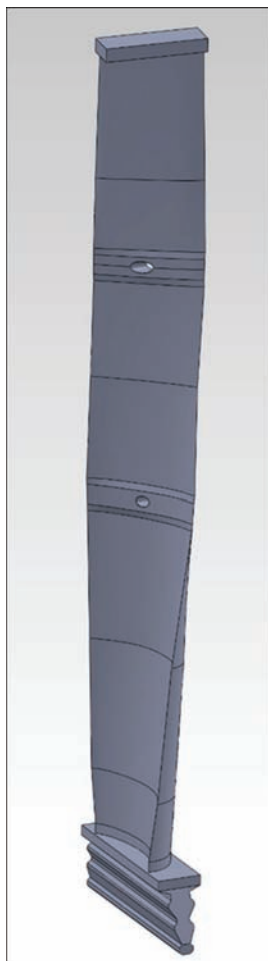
Общий вид рабочей лопатки пятой ступени цилиндра низкого давления (ЦНД) паровой турбины типа К-1000-60/3000
